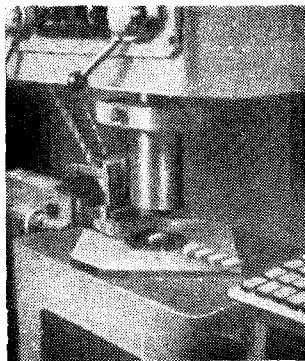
Механический пресс для изготовления твердосплавных пластинок
